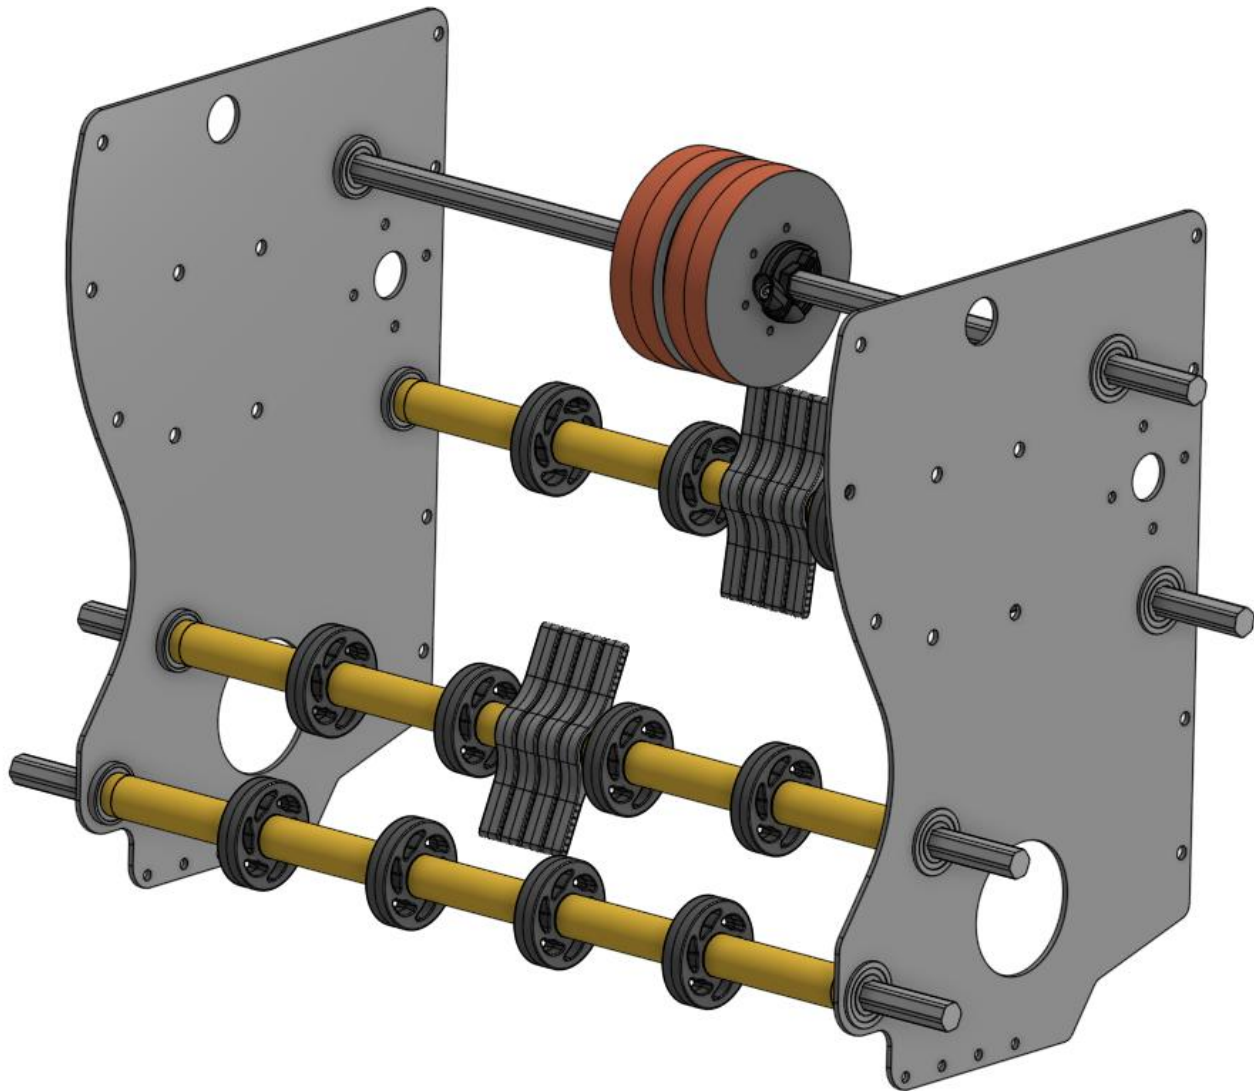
Llanta Flywheel del Lanzador (colocado entre las ruedas de sigilo)
